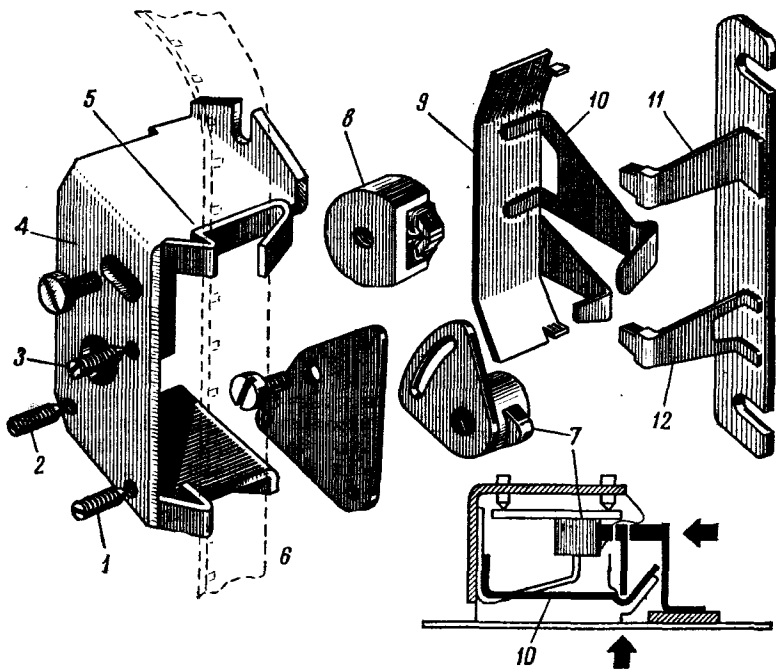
Конструкция блока магнитных головок: 1, 2, 3 — регулировочные винты; 4 — корпус; 5, 6 — направляющие колонки; 7 — универсальная головка; 8 — стирающая головка в корпусе; 9, 10 — пружина; 11, 12 — прижимное устройство
